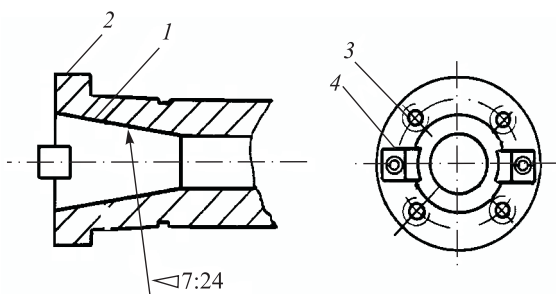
Передняя часть шпинделя фрезерного станка
